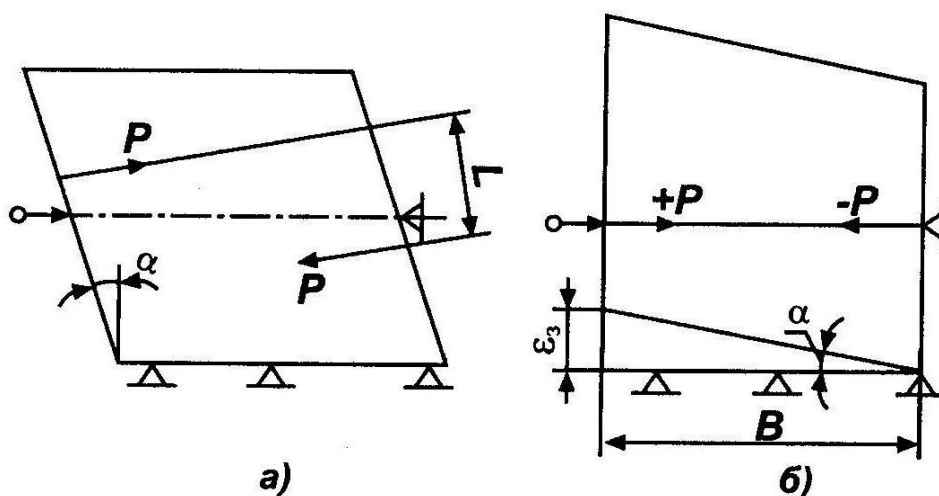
Схема повороту заготовки при закріпленні:
